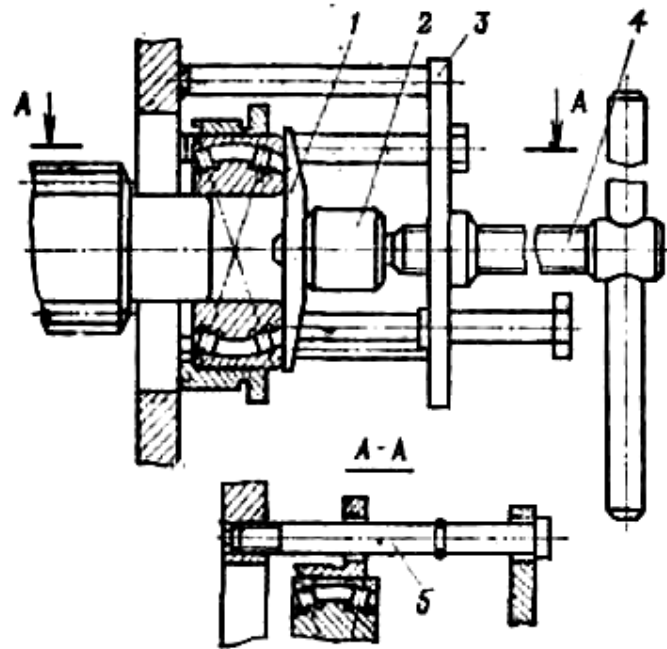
Пристосування для встановлення заднього підшипника проміжного вала І-801.31.000:
